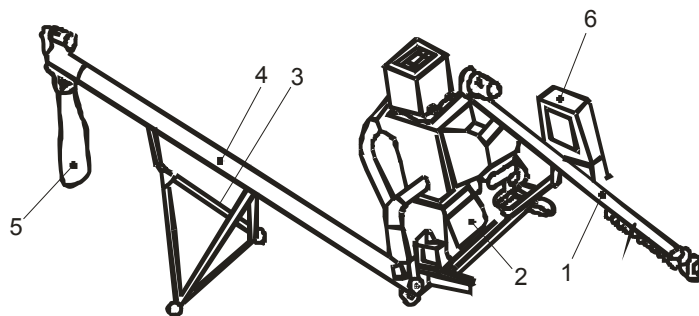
Общий вид комплекта оборудования дробилки безрешетной ДБ-5-1: 1 – шнек загрузочный; 2 – дробилка; 3 – подставка; 4 – шнек выгрузной; 5 – рукав; 6 – шкаф управления.
